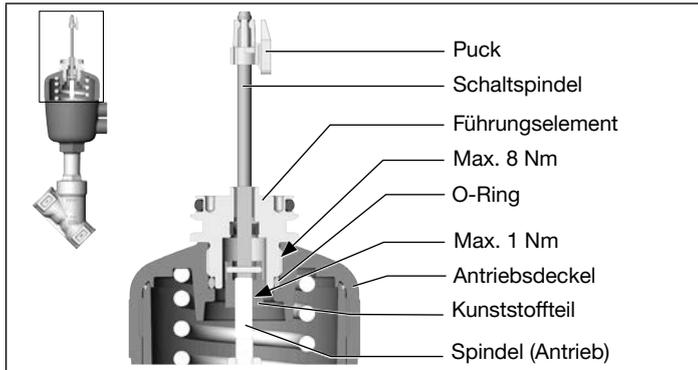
Schaltspindel montieren (2), externe Steuerluftführung
